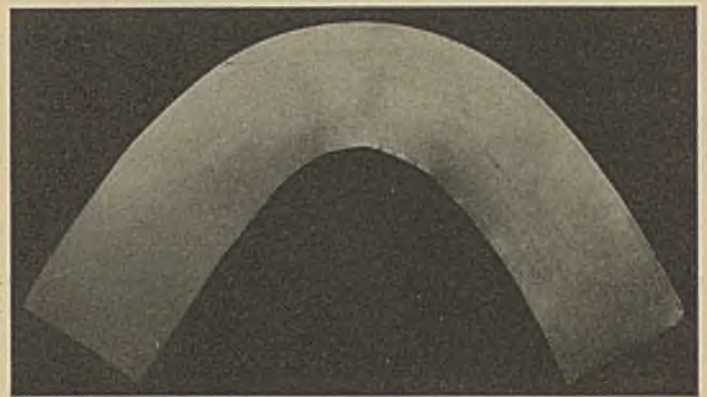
Biegeprobe einer Schweißnaht (Blechstärke 88 mm).
